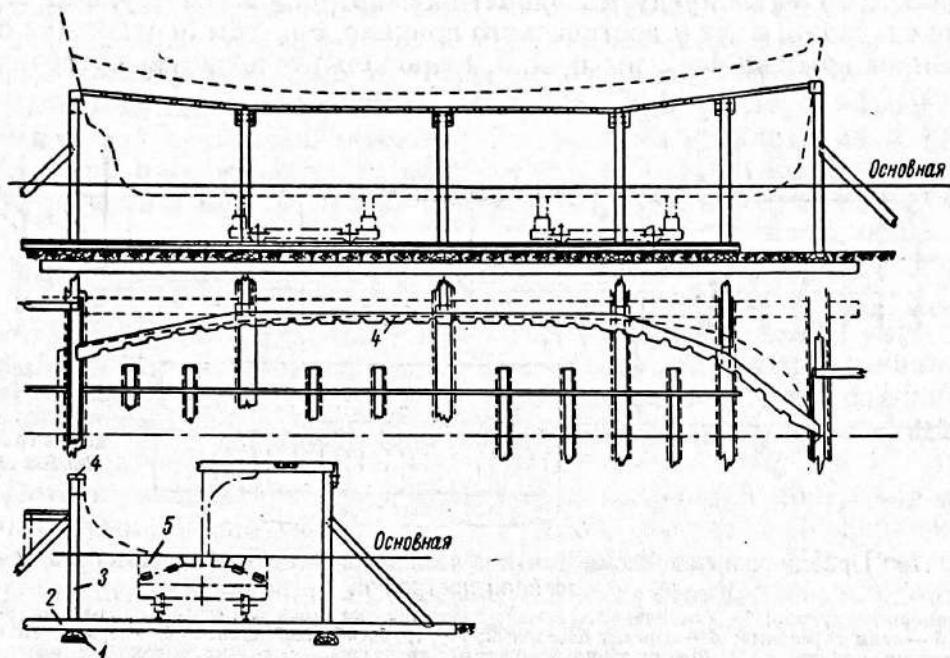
Стапель-кондуктор для закладки корпуса мотобота.
